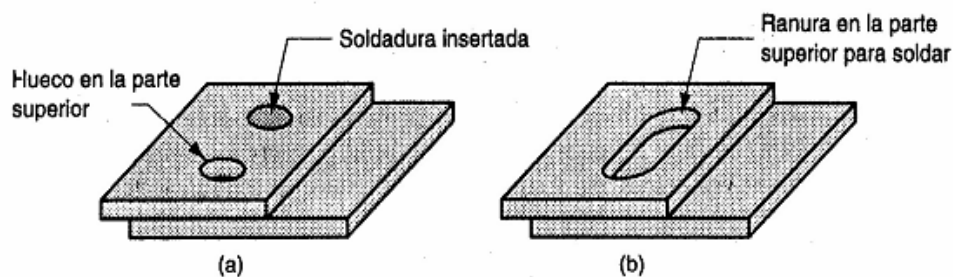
(a) Soldadura con inserto y (b) soldadura en ranura.
